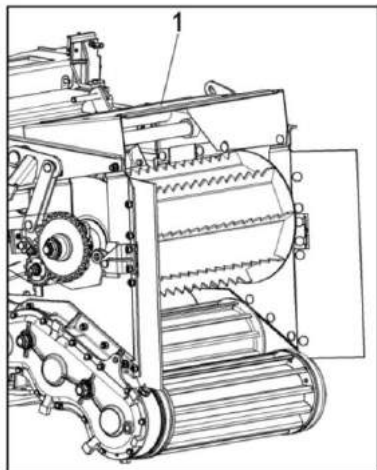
Рама барабана с устройством для дробления зерна
